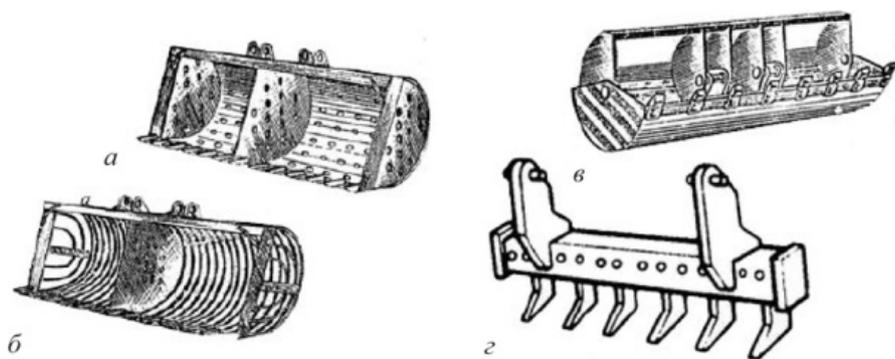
Виды сменных рабочих органов циклического действия: а — решетчатый ковш; б — решетчатый ковш с удлиненными зубьями; в — уширенный поворотный самоочищающийся ковш; г — корчующий рабочий орган
